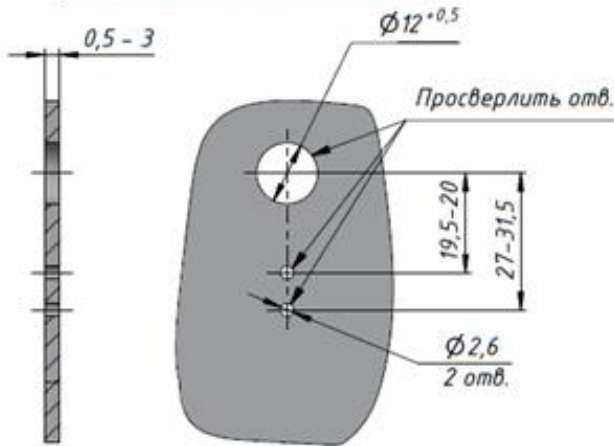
Габаритные и установочные размеры угольника 745222.020
